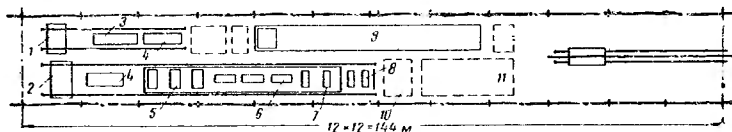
Габаритная схема технологической планировки УТП-1 производства доборных железобетонных конструкций для домов серии 1-464А (04-09-3)
